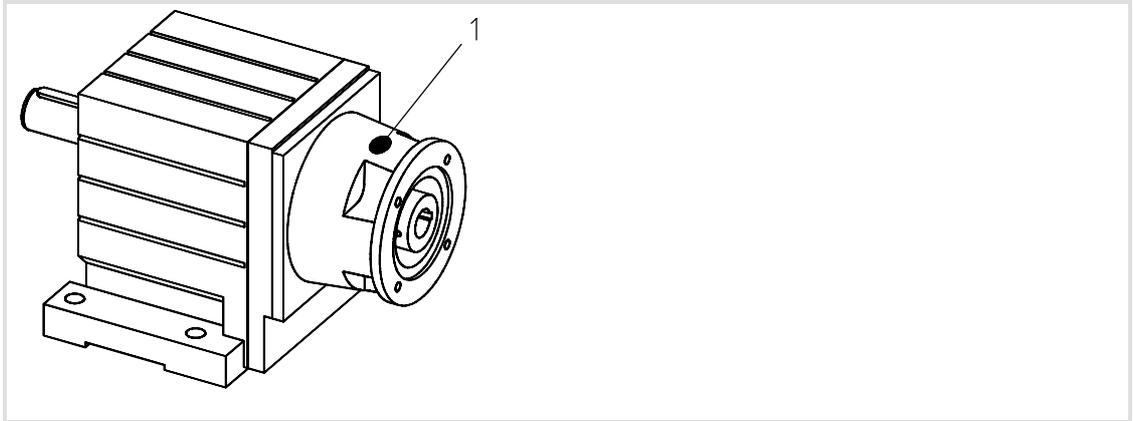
Стандартный электродвигатель GNA с фланцем, местоположение резьбовой пробки (1)
